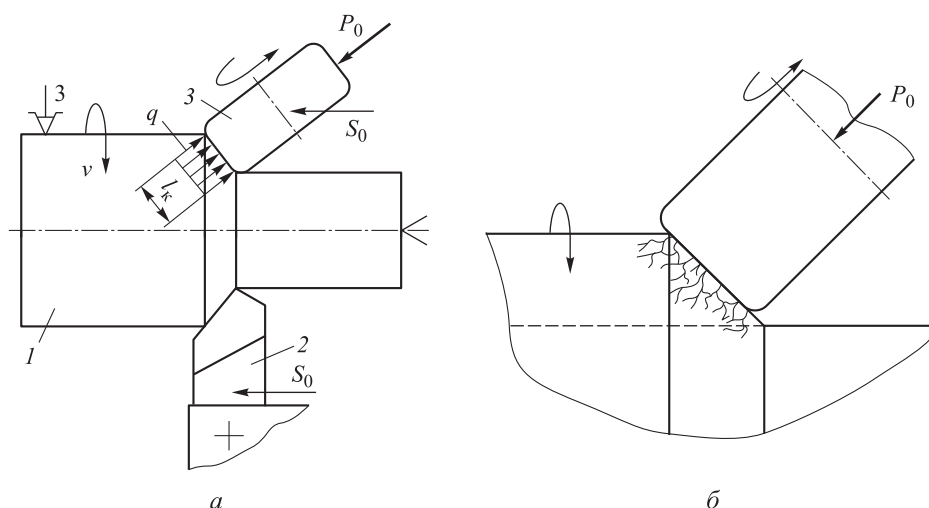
Схема точения с предразрушением материала срезаемого слоя (а) и характер разрушения поверхности резания при воздействии силы P_0 нагружающего устройства (б): 1 — заготовка; 2 — режущий инструмент; 3 — накатной ролик; q — линейная нагрузка дополнительного устройства на срезаемый слой ($q = P_0 / l_k$, где P_0 — сила воздействия накатного ролика; l_k — длина контакта рабочего участка ролика и заготовки)
